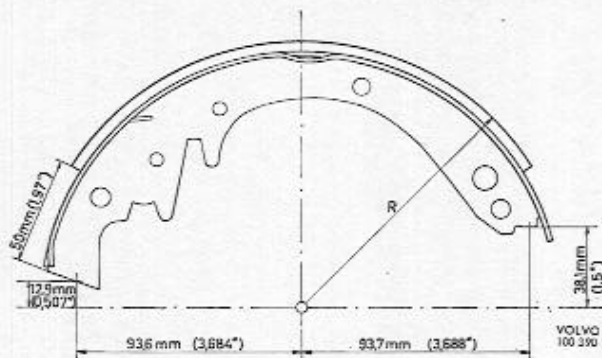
Einstellmaß für die hintere Bremsbacke der Hinterradbremse
